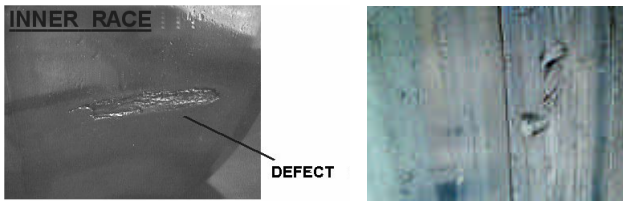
Defecto localizado en la pista interna(izquierda), y superficie del eje sobre la cual se apoya el rodamiento (derecha).
